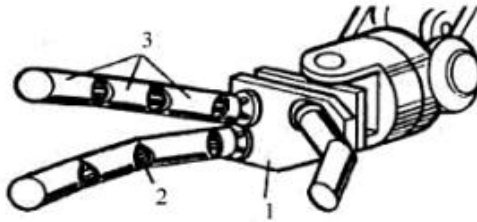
Захватний пристрій з тросовим механізмом:
